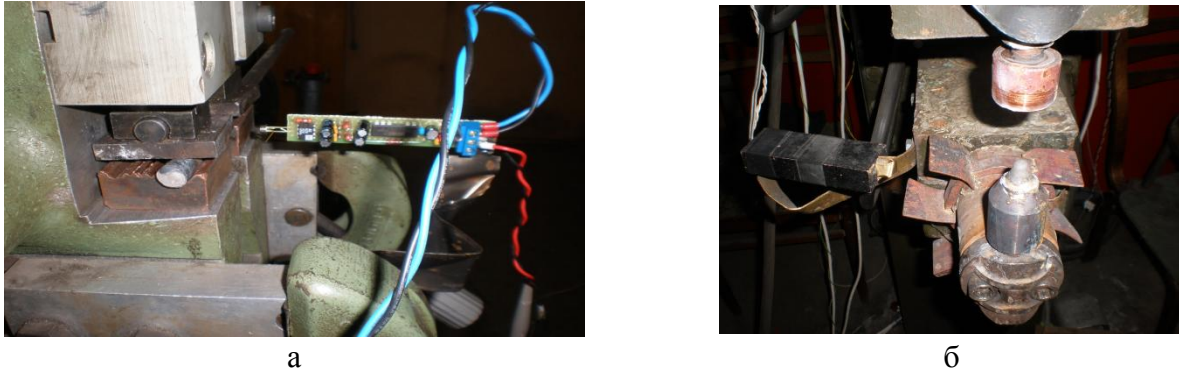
Дослідний зразок вимірювача з сенсором типу TS318-11C55: а – без захисного корпусу; б – в металевому захисному корпусі
